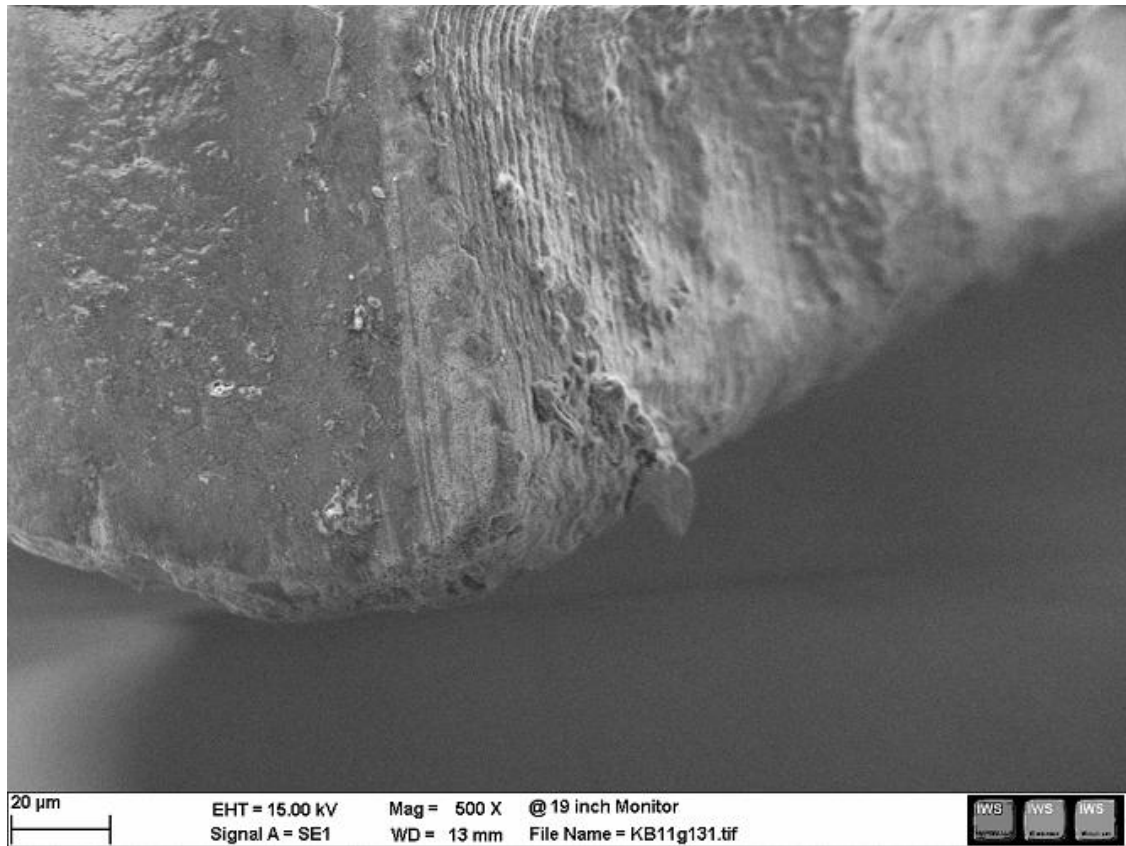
Detail X; Brasseler ZrO₂ CeraDrill; 111 Bohr. Hand; REM (500X)
